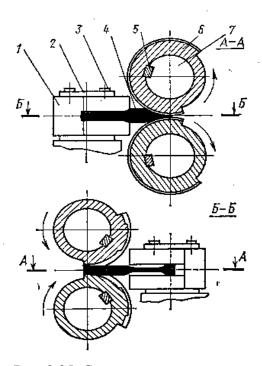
Схема непрерывной вальцовки заготовок в двух-клетьевых ковочных вальцах: 1 — валок первой клети; 2 —крышка; 3 — болт; 4 — профилируемая заготовка; 5 — шпонка; 6 — валок второй клети; 7 — вал второй клети
